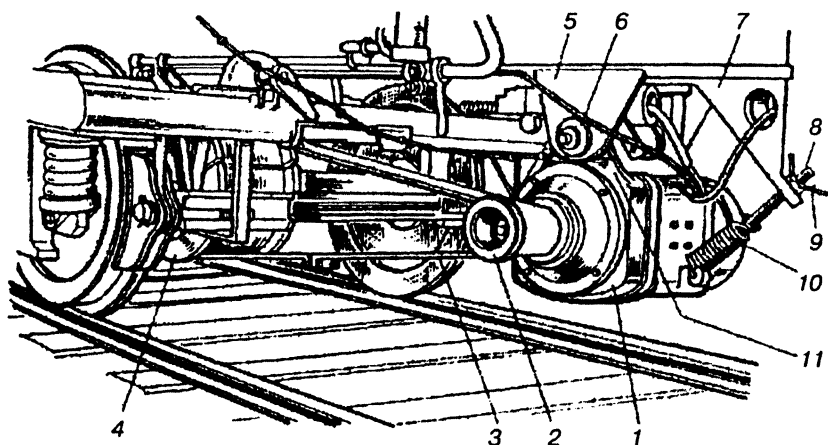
Плоскоременный привод генератора РД-2Д:
